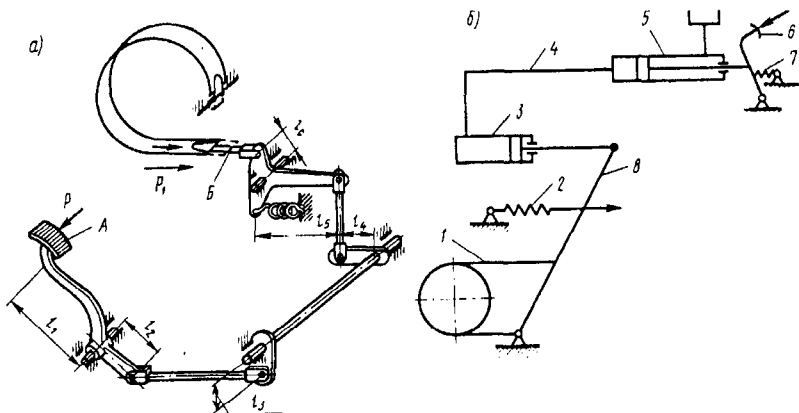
Схемы управления ленточным тормозом непосредственного действия; 1 – тормозная лента; 2 – пружина; 3 – рабочий цилиндр; 4 – трубопровод; 5 – гидравлический цилиндр; 6 – педаль управления; 7 – пружина; 8 – рычаг.
